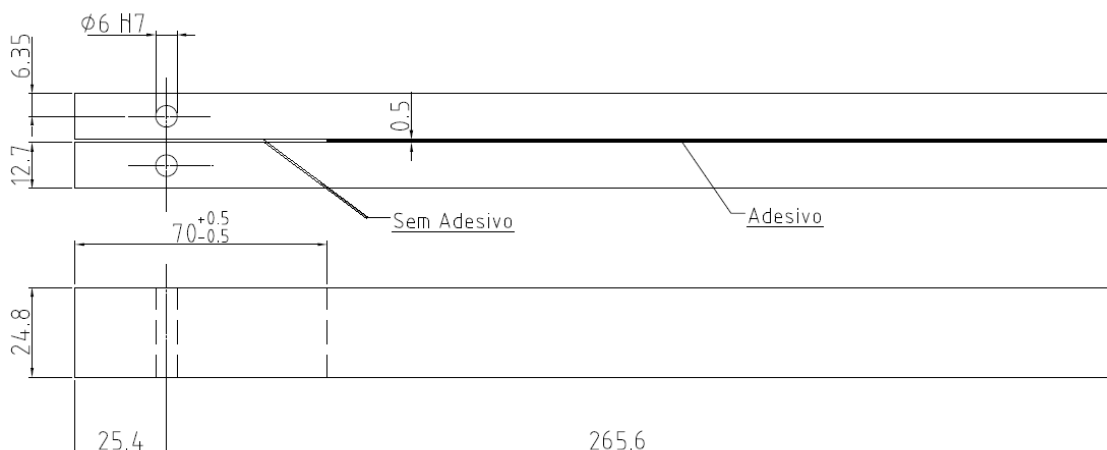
Geometria do ensaio DCB (dimensões em mm)
